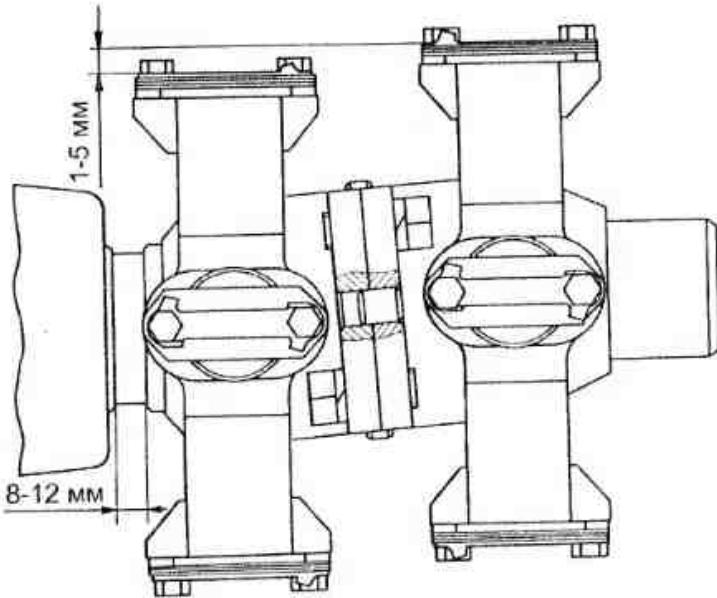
Схема проверки расположения крестовин карданного вала
